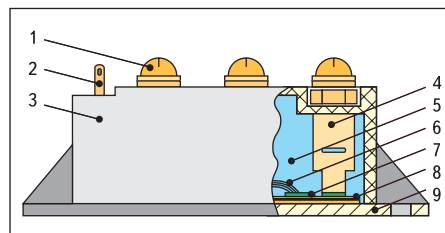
Сборочный чертеж силового модуля паяной конструкции:
